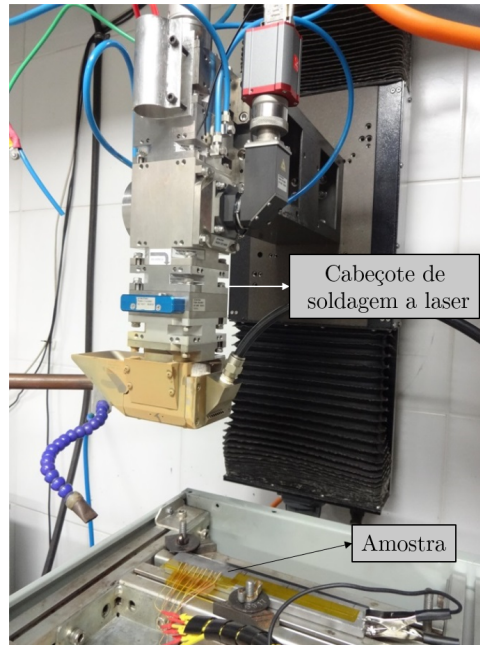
Bancada experimental com o cabeçote de soldagem a LASER, amostra com os termopares posicionados e aspecto superficial do cordão de solda.
